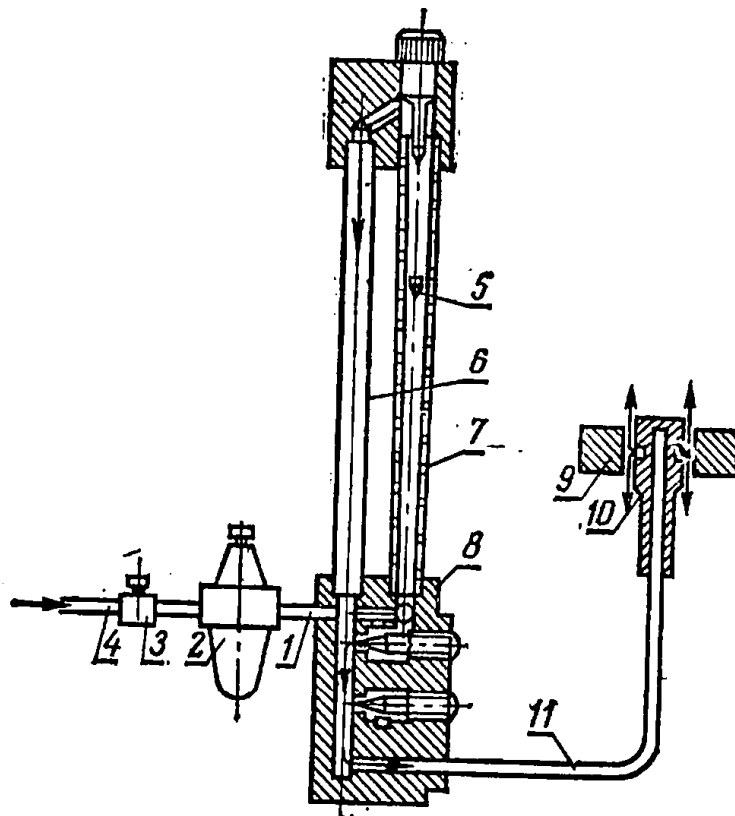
Схема пневматического длиномера с пробкой для внутренних измерений:
